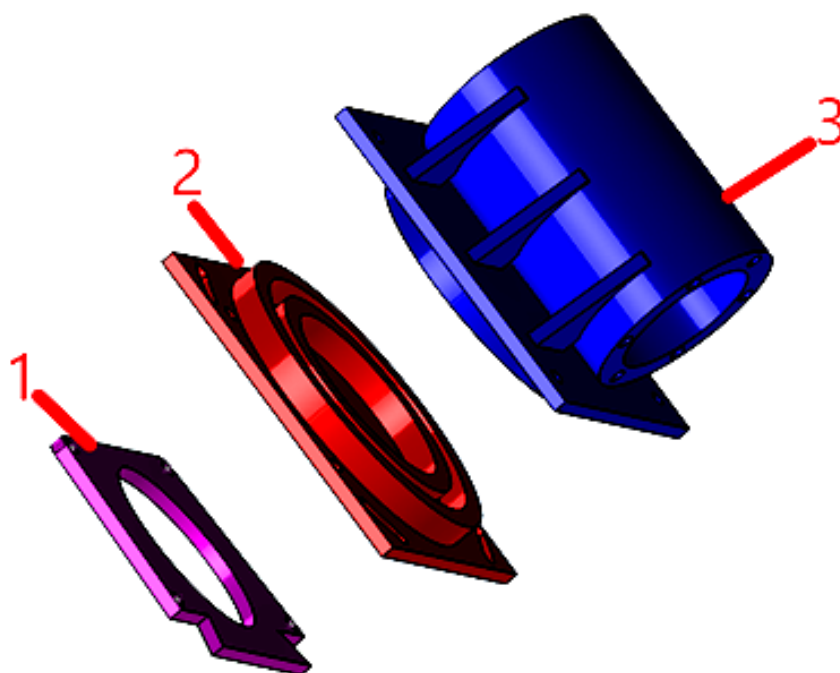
рознесений вид вузла для встановлення мотор шпинделя на консоль верстата: 1- плита, яка кріпиться на верстат; 2 - базова деталь для установки зварного корпусу шпинделя; 3 - зварний корпус шпинделя
